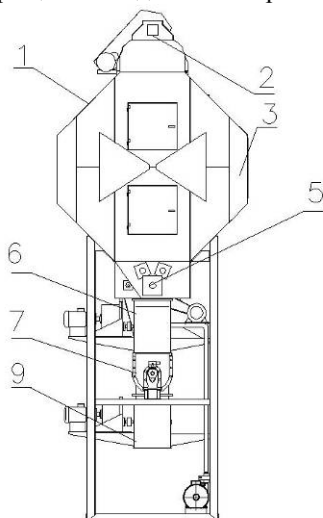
Схема установки для сушки и вакуумного охлаждения зерна (вид сбоку)
